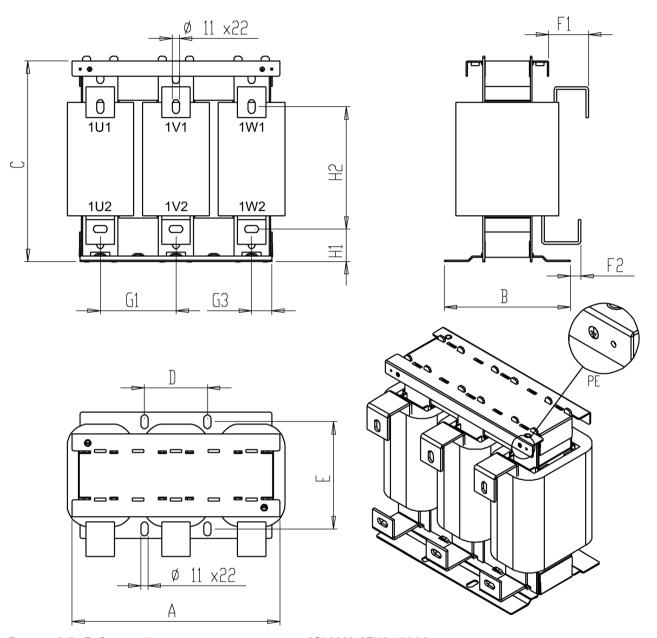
Габаритный чертеж сетевого дросселя 6SL3000-0EH34-7AA0
